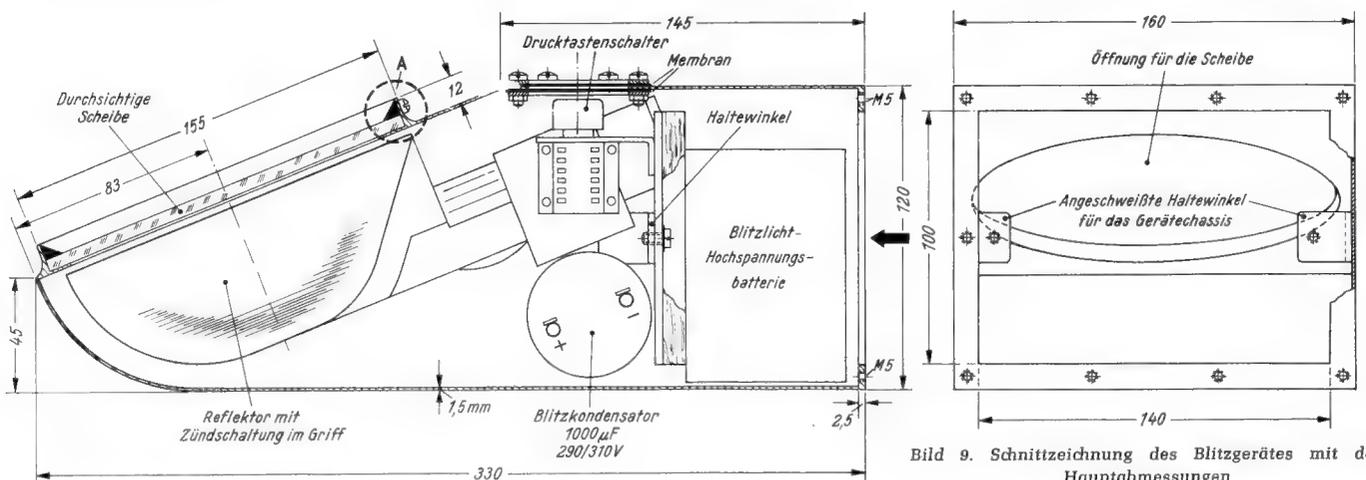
Schnittzeichnung des Blitzgerätes mit den Hauptabmessungen
